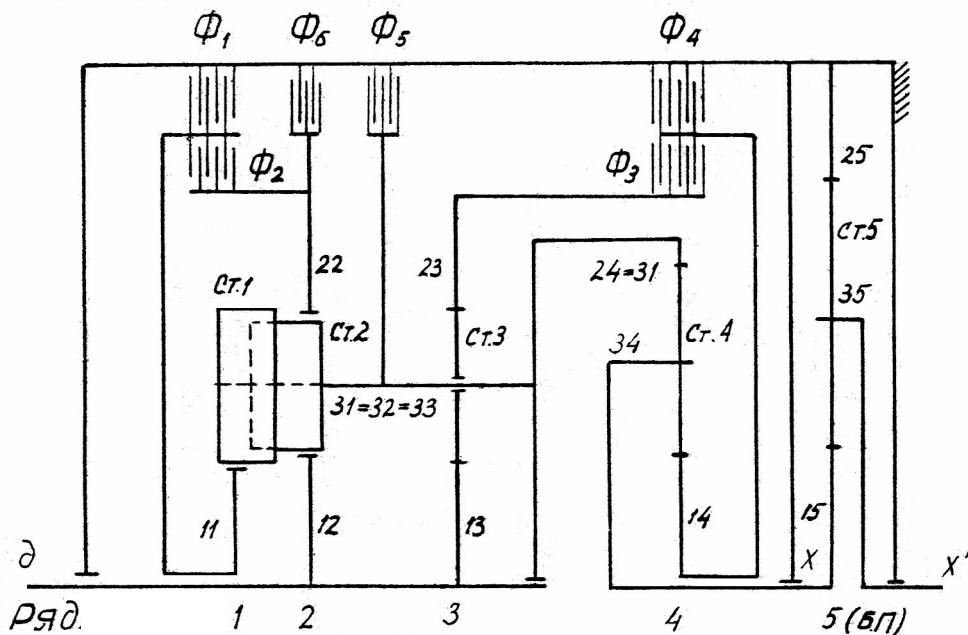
Кінематична схема планетарної коробки передач танків Т-64 і Т-72
